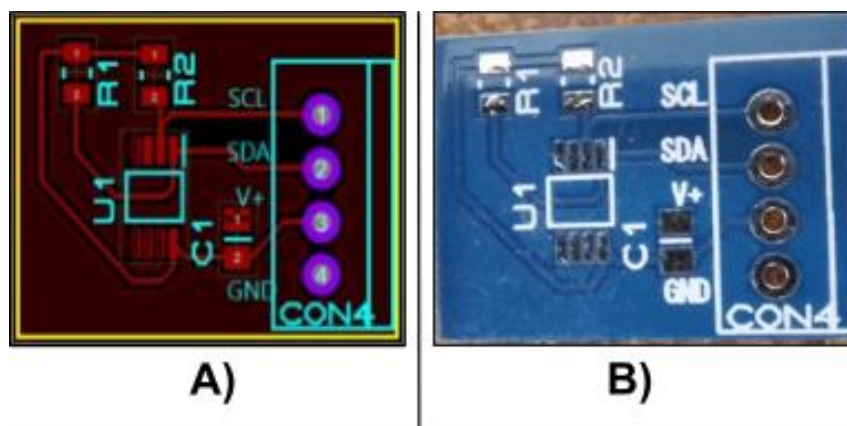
A) Diseño en PROTEUS del sensor digital y B) PCB del TM75.
